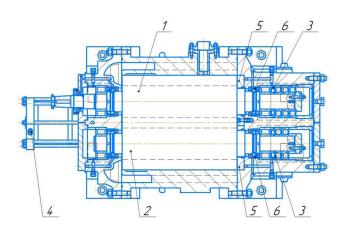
Компрессор винтовой: 1 – ведущий ротор, 2 – ведомый ротор, 3 – подшипниковый узел, 4 - гидропривод, 5 – вставки, 6 – уплотнение
